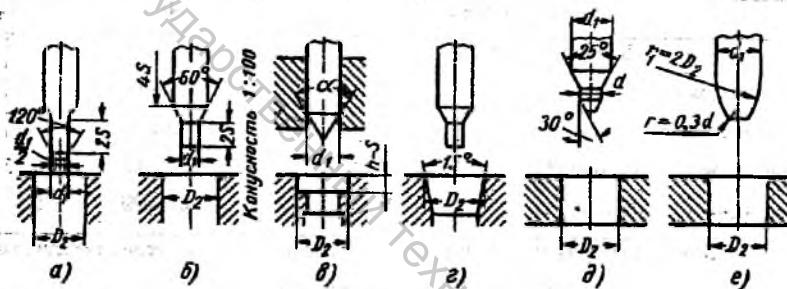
Схема рабочих частей штампов для отбортовки
